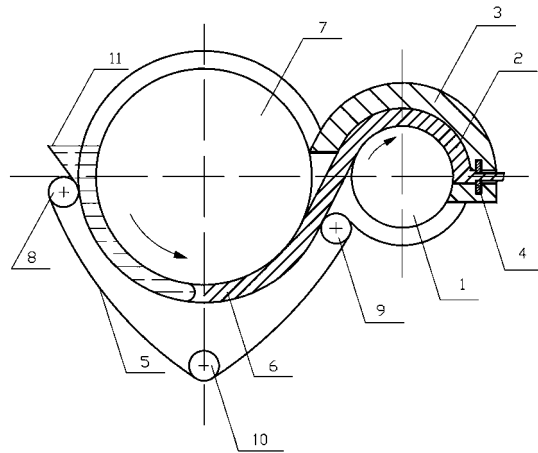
Схема процесса непрерывного литья и прессования металлов
